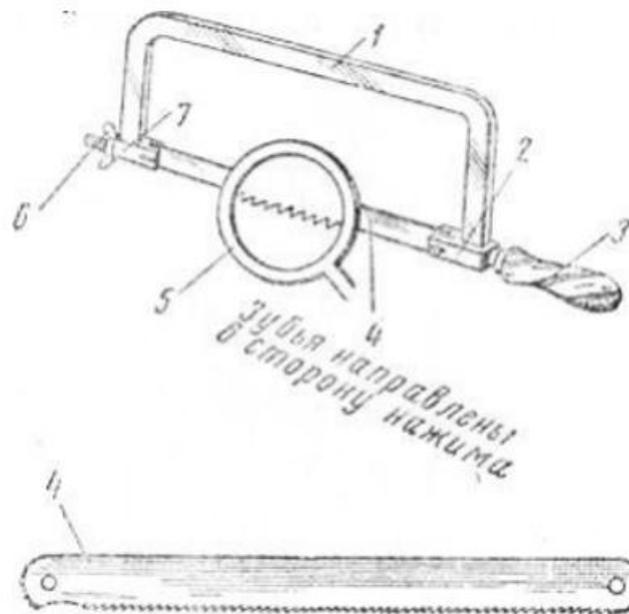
Ножовка: 1 - станок, 2 - неподвижная серьга, 3 - рукоятка, 4 - ножовочное полотно, 5 - лупа, 6 - барашек, 7 - подвижная серьга
